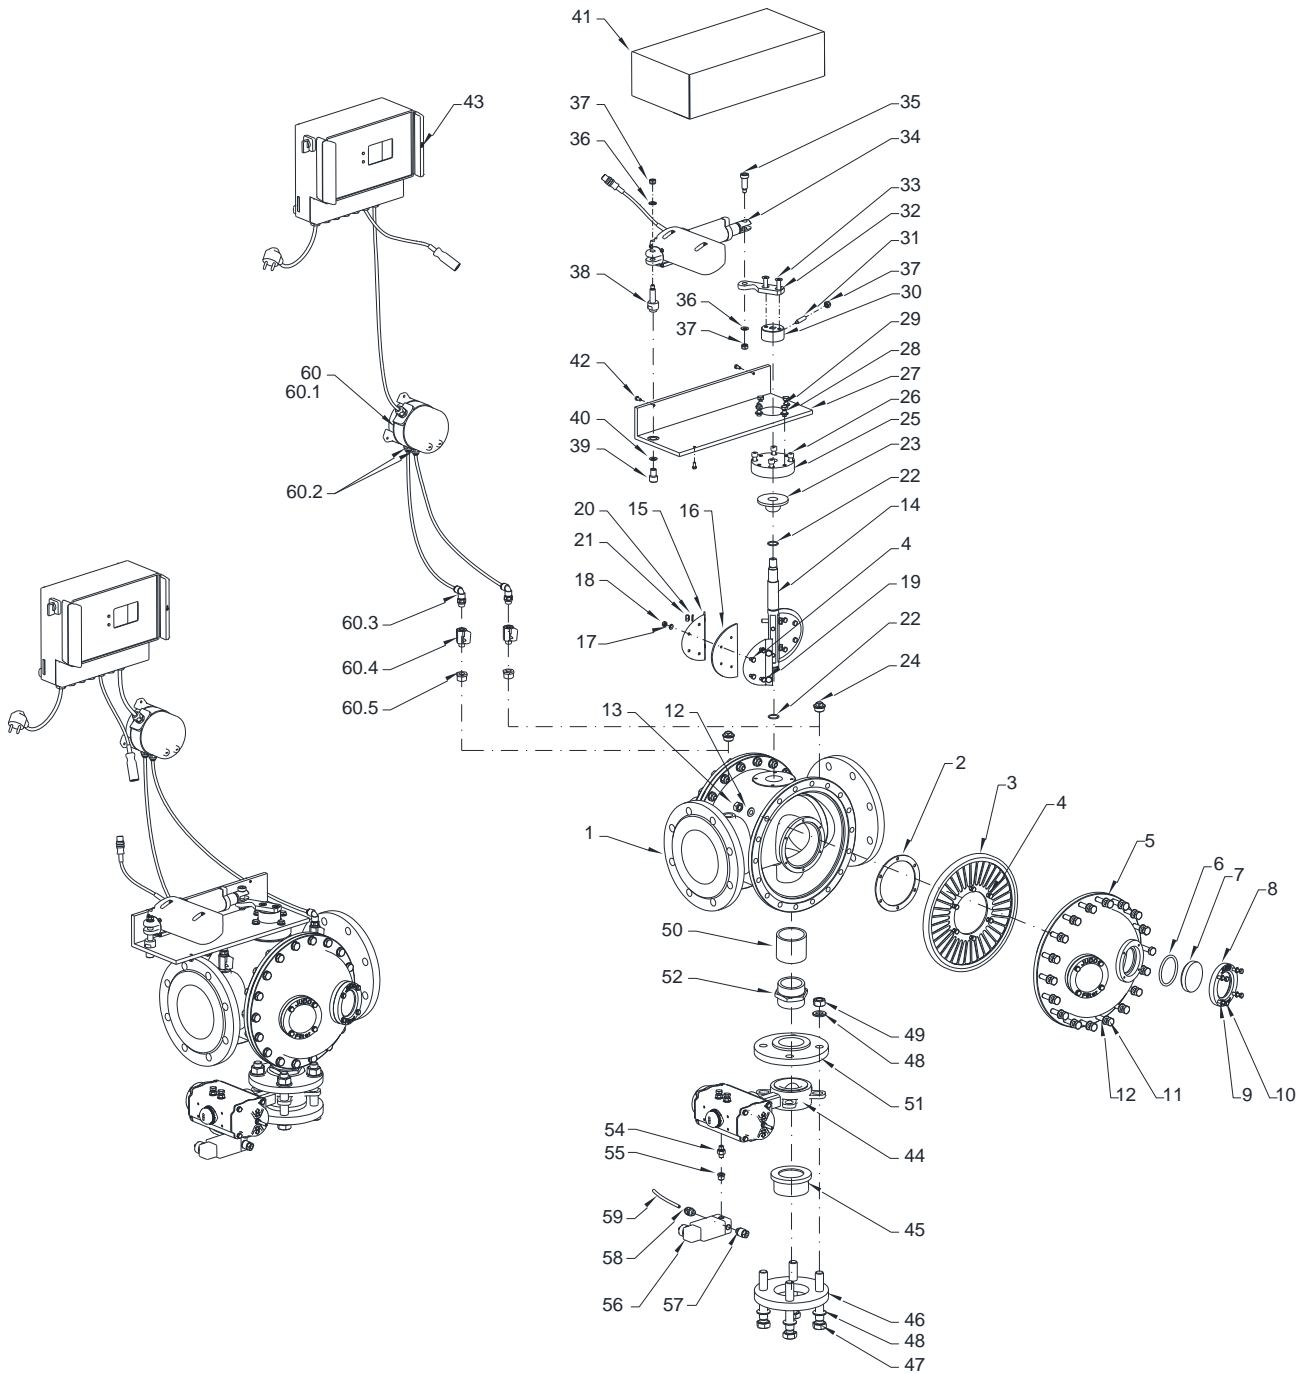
Explosionszeichnung JRSF-ATP DN125
